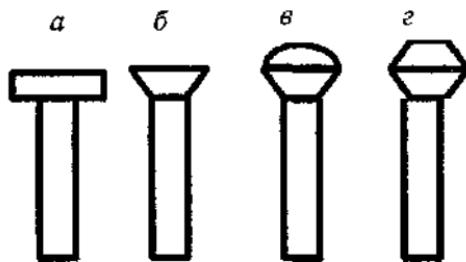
Виды заклепок: а — с плоской головкой; б — с по-тайной головкой; в — с полупотайной головкой; г — коническая заклепка с подголовкой.
